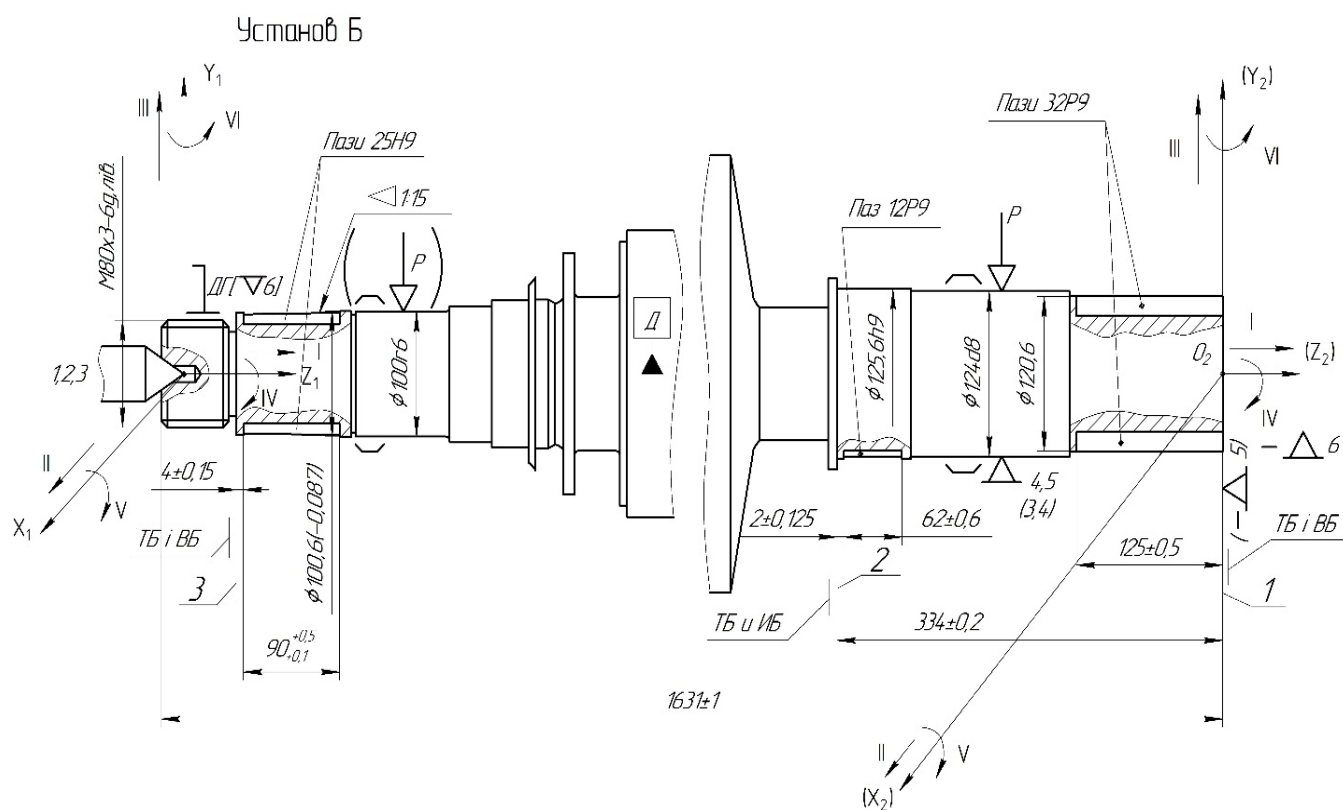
5 – Схеми установки заготовки на операції 030. В дужках схема №2
